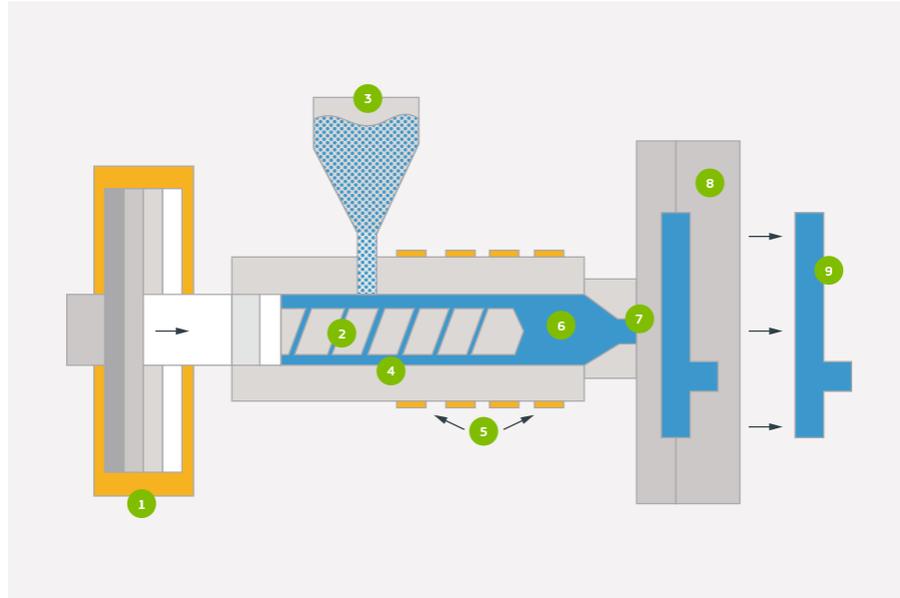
Proceso de moldeo por inyección. Fuente: www.protolabs.es
